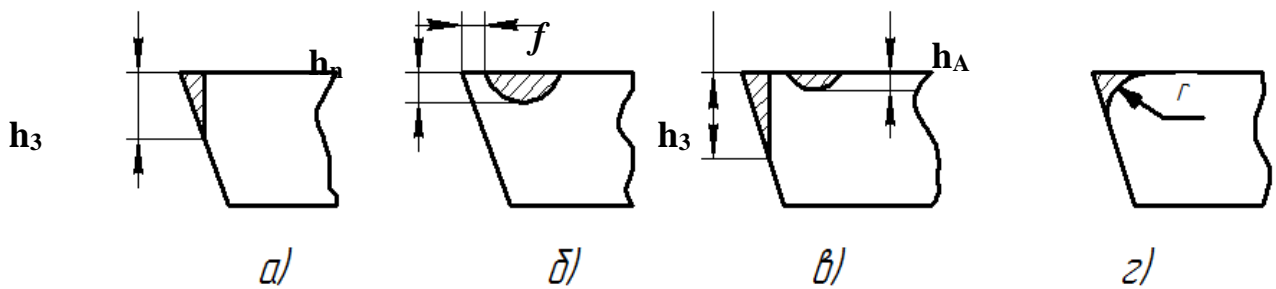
Основні форми зносу різальної частини інструмента: а-по задній поверхні; б-по передній поверхні; в-по задній і передній поверхнях; г-плавне заокруглення
